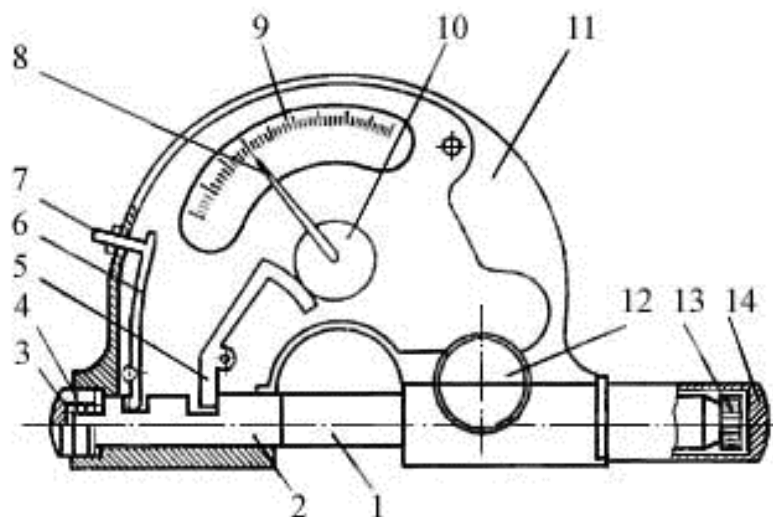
Схема рычажной скобы: 1 – регулируемая пята; 2 – подвижная пята; 3 – колпачок; 4 – пружина; 5 – малое плечо рычага; 6 – рычаг арретира; 7 – арретир; 8 – стрелка; 9 – шкала; 10 – триб; 11 – корпус; 12 – зажим; 13 – головка; 14 – предохранительный колпачок
